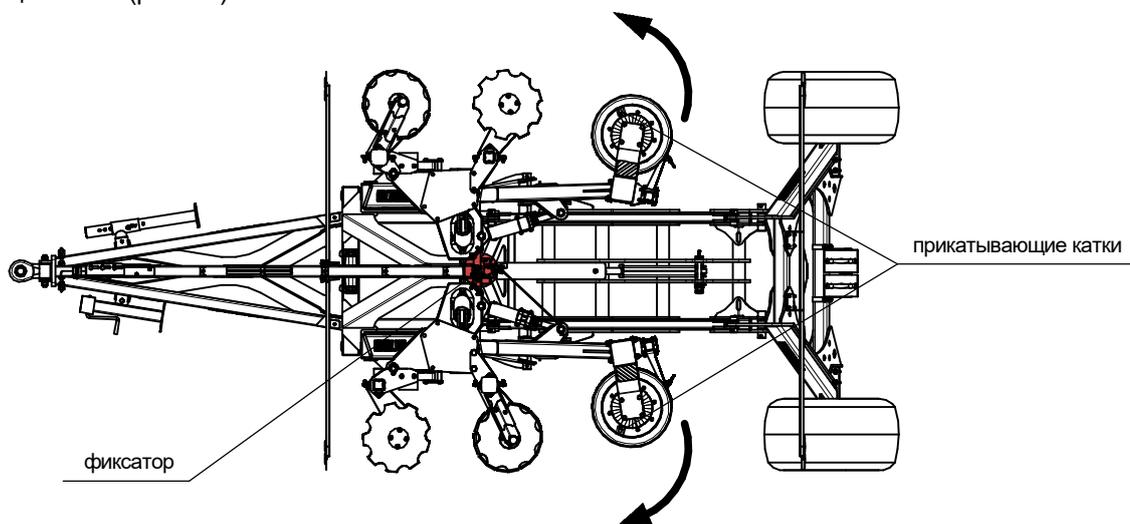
Разведение прикатывающих катков дисковой почвообрабатывающей машины ДПМ "Универсал" / "Универсал Т" (вид сверху)
